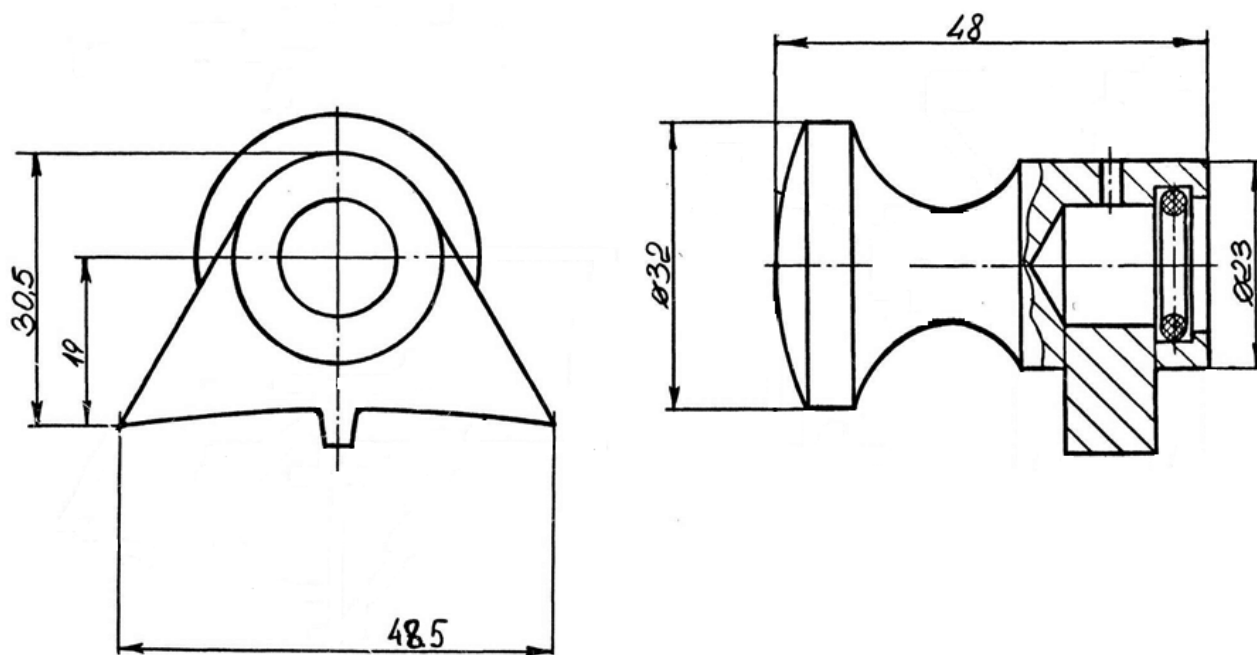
3М 7820-4550, Фиксатор коленчатого вала
